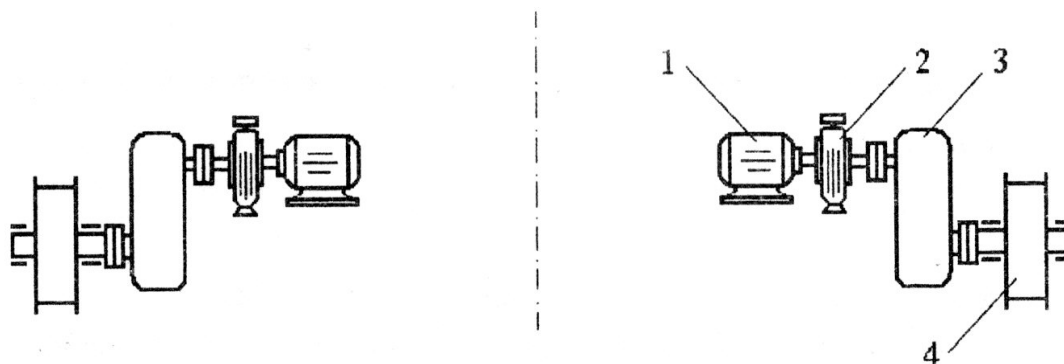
Конструктивна схема пересування мостового крана з роздільним приводом
